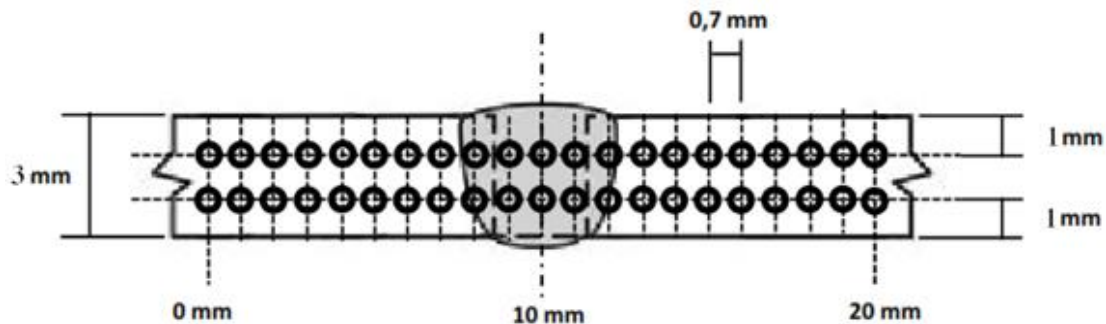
Posicionamento dos pontos para determinação do perfil de dureza da junta soldada.
